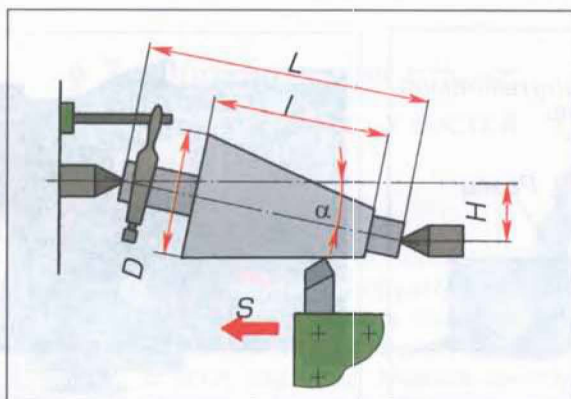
Получение конусной поверхности на детали путём смещения корпуса задней бабки:  $L$  – длина детали,  $l$  – длина конуса,  $H$  – смещение задней бабки от основной оси,  $D$  – диаметр конуса,  $S$  – направление движения резца,  $\alpha$  – угол уклона конуса
